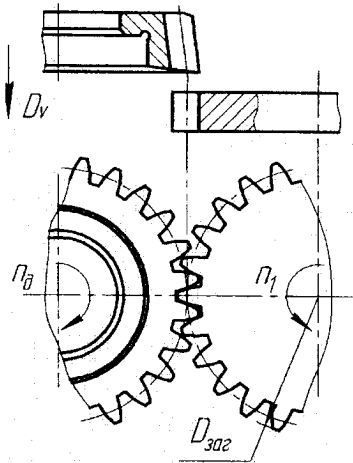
Нарізування довбачем зубів на циліндричному колесі:
